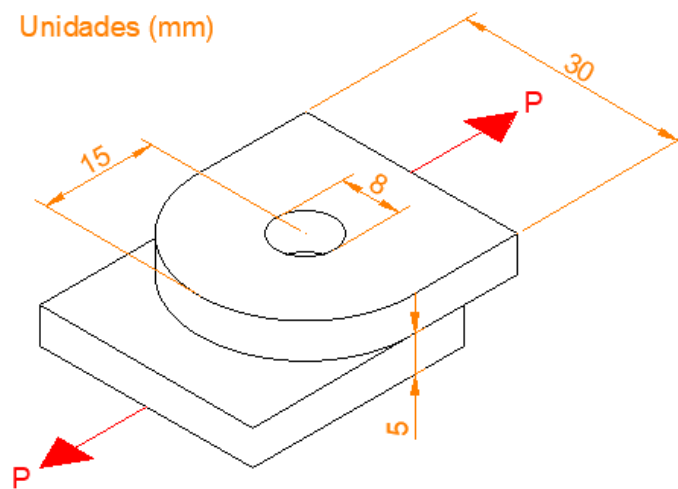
Esquema para esfuerzo de aplastamiento en placa. [Autor]
